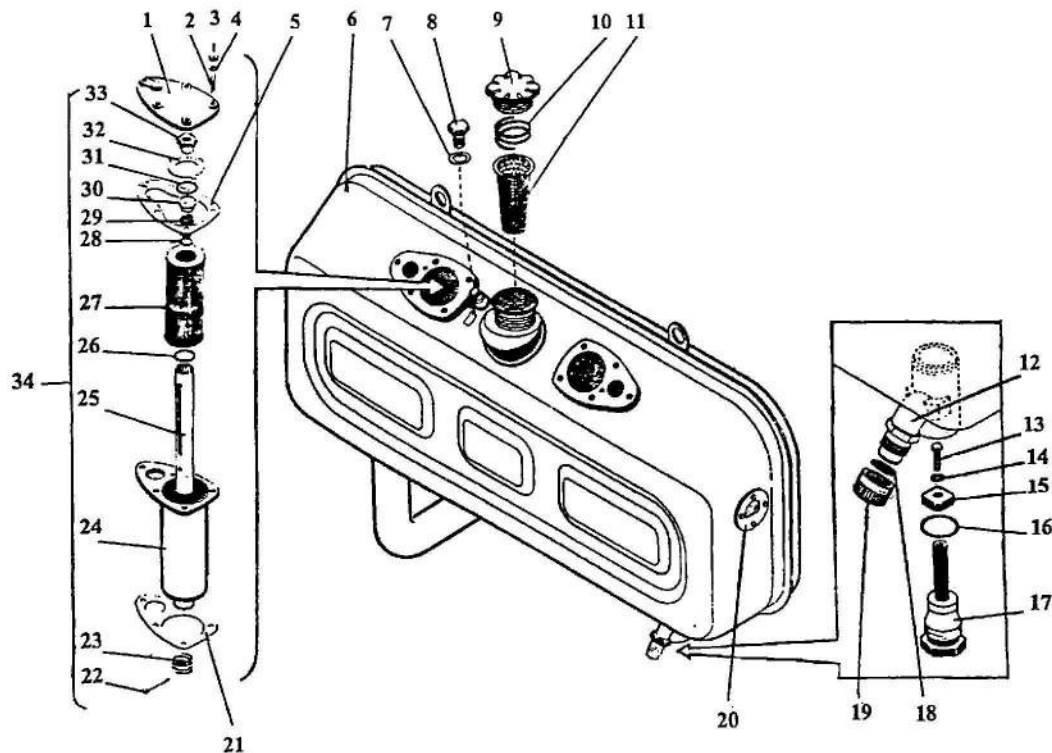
Гидробак. 1 - крышка; 2 - шпилька; 3 - гайка; 4, 14, 28, 32 - шайба; 5, 7, 18, 21 - прокладка; 6 - корпус бака; 8, 17 - пробка. 9 - крышка; 10, 23, 29 - пружина; 11 - фильтр; 12 - штуцер; 13 - болт; 15 - магнит; 16, 26, 31 - кольцо; 19 - колпачок; 20 - смотровое окно; 22 - шплинт; 24 - корпус фильтра; 25 - труба; 27 - фильтрующий элемент; 30 - клапан; 33 - гнездо клапана; 34 - фильтр в сборе
